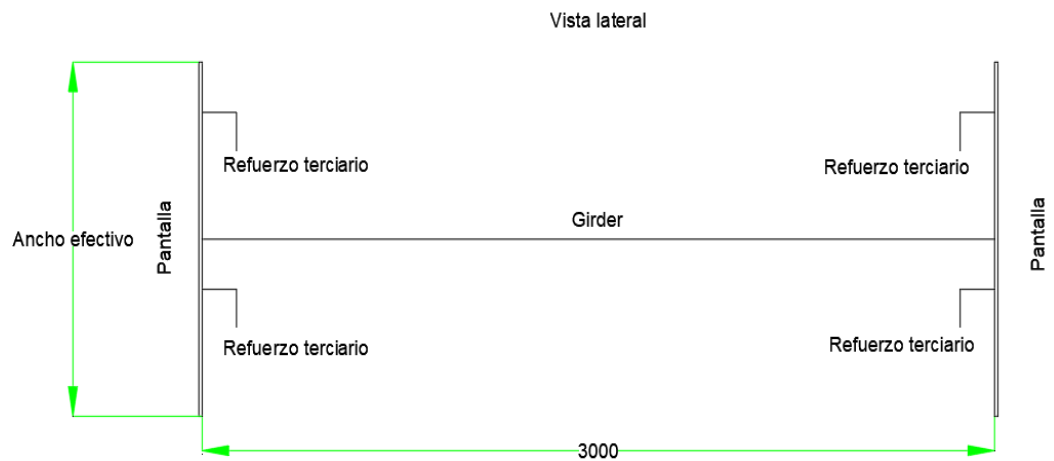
Vista lateral del diagrama de refuerzo principal o girder
